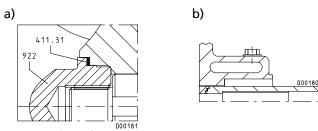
a) Laufradbefestigung an Lagerträger P08s und b) Intensiv gekühlter Wellendichtungsraum
